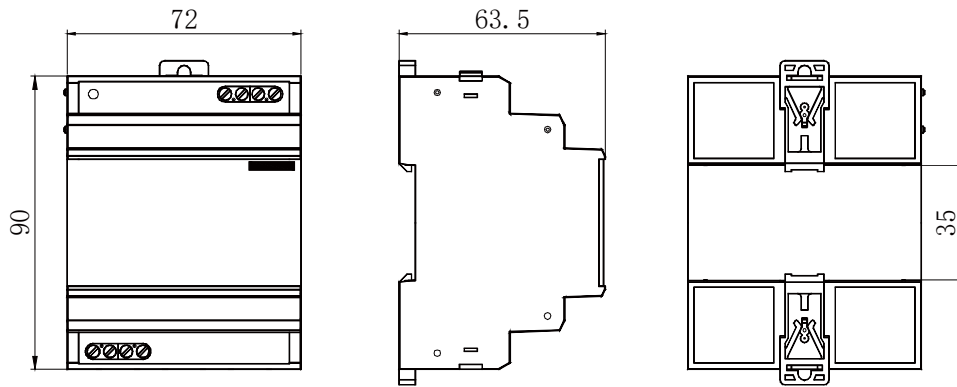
Внешний вид и габаритные размеры модуля питания P
